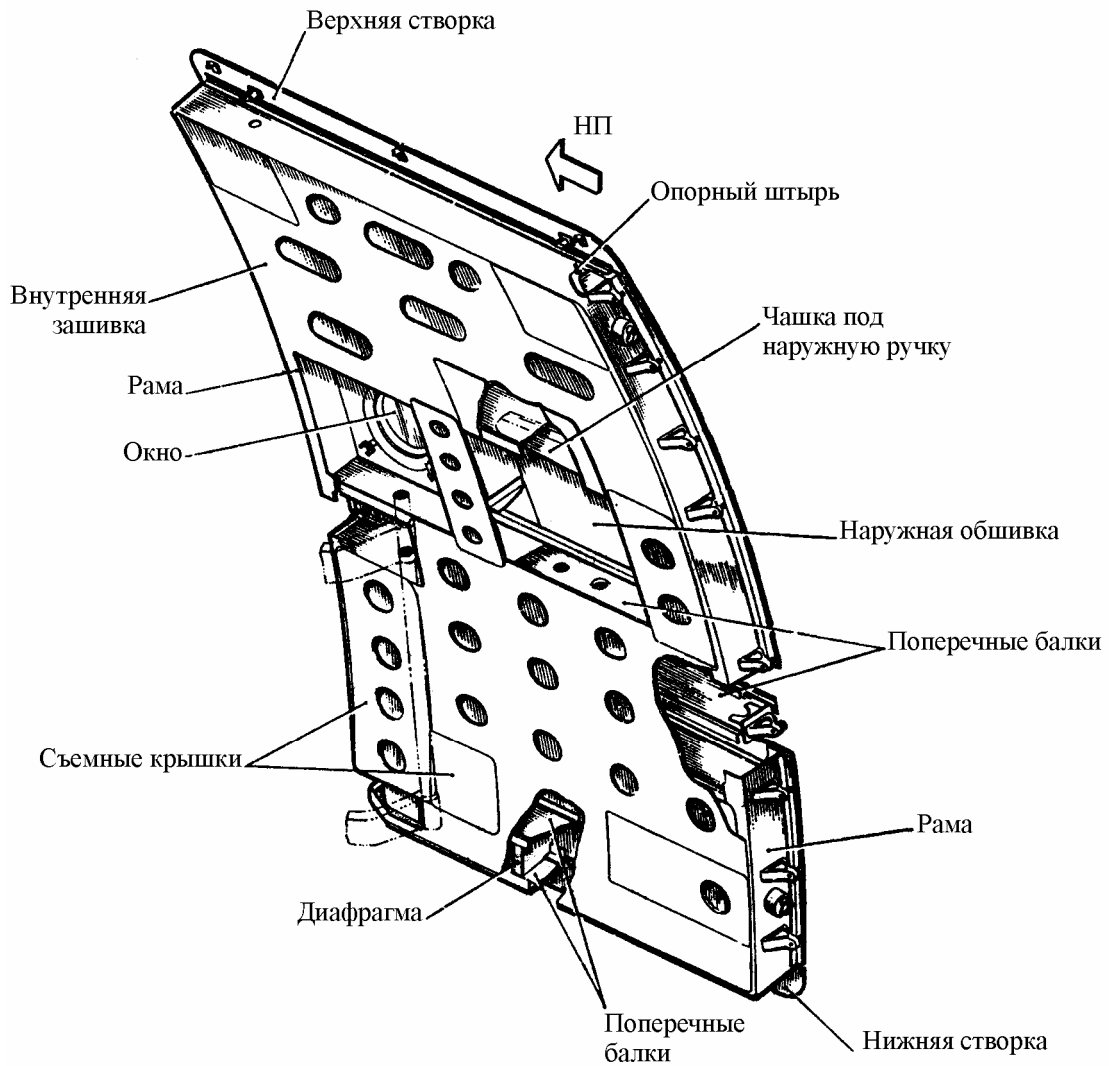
Крышка аварийной двери (вид изнутри фюзеляжа на правый борт)
